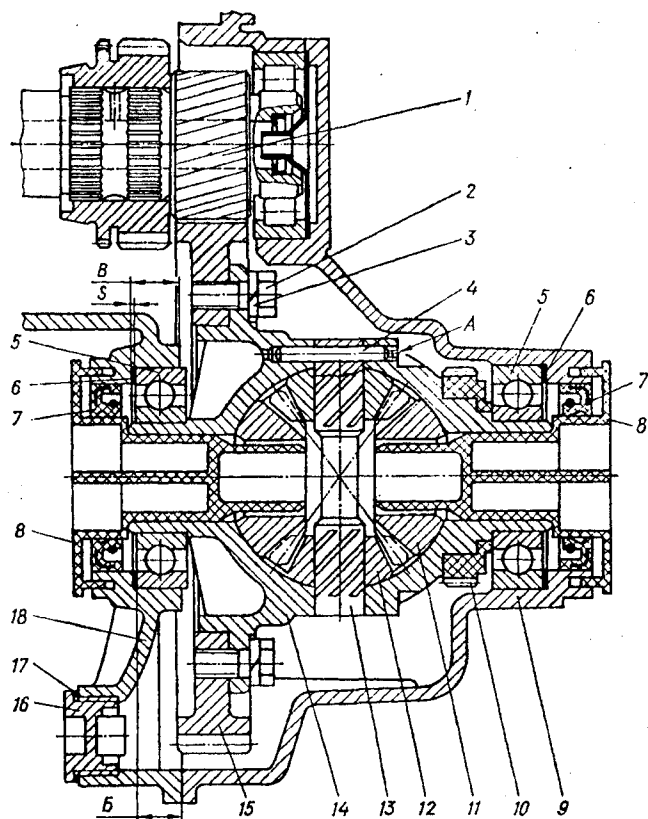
Главная передача с дифференциалом: 1 – шестерня ведущая главной передачи; 2 – болт; 3 – шайба пружинная; 4 – штифт; 5 – шариковый подшипник дифференциала; 6 – регулировочная прокладка; 7 – манжета; 8 – транспортная крышка; 9 – картер сцепления; 10 – ведущая шестерня привода спидометра; 11 – шестерня полуоси; 12 – сателлит дифференциала; 13 – ось сателлитов дифференциала; 14 – коробка дифференциала; 15 – шестерня главной передачи; 16 – сливная пробка; 17 – прокладка; 18 – картер коробки передач; А – после запрессовки штифта – кернить
